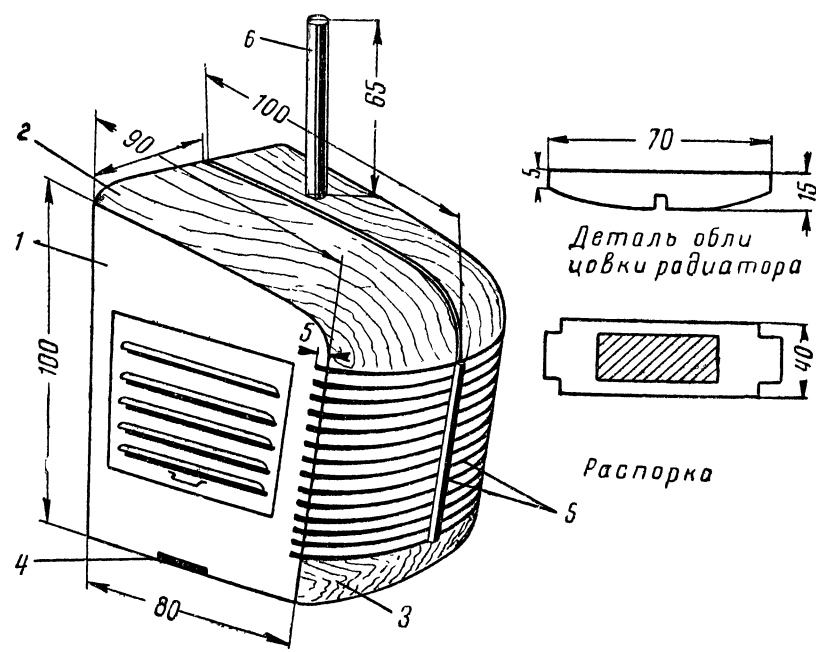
Капот: 1—боковинка капота; 2—верхний брусок; 3—нижний брусок; 4—распорка; 5—детали облицовки радиатора; 6—выхлопная труба
